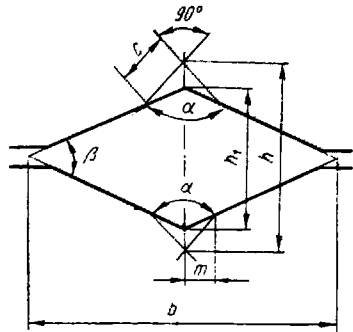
Предчистовой калибр для прокатки квадратной стали с острыми углами
